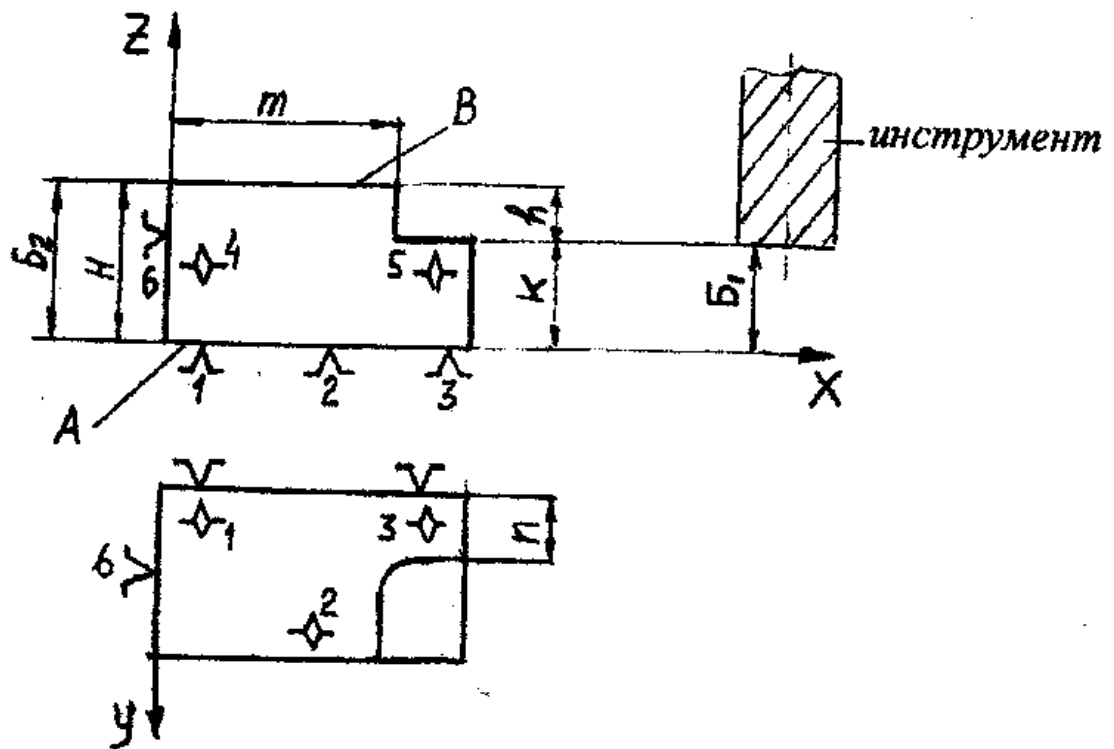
Схема базирования заготовки в координатный угол и настройка инструмента.
